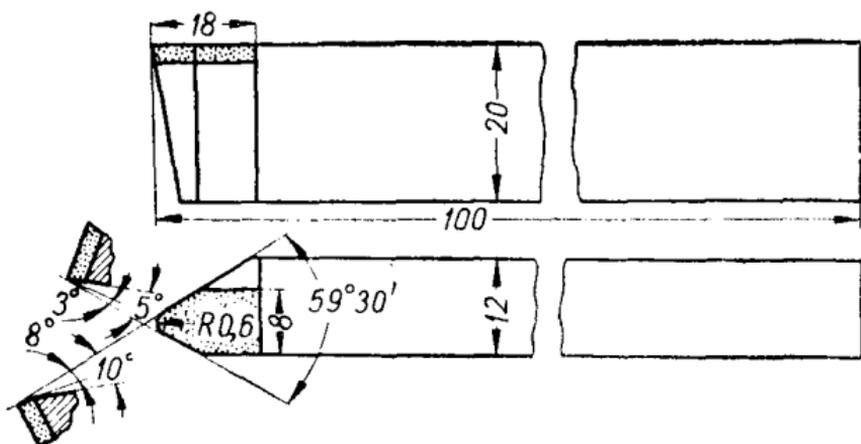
Резьбовой резец для нарезания правой метрической резьбы.
